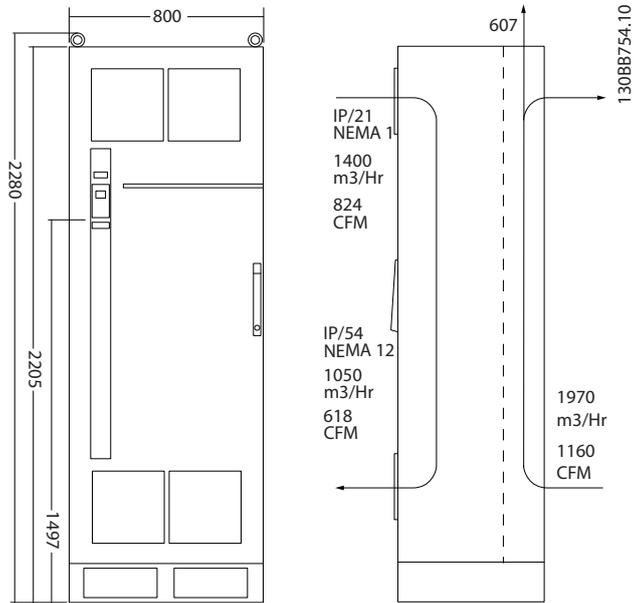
Dimensiones mecánicas (mm), F8
